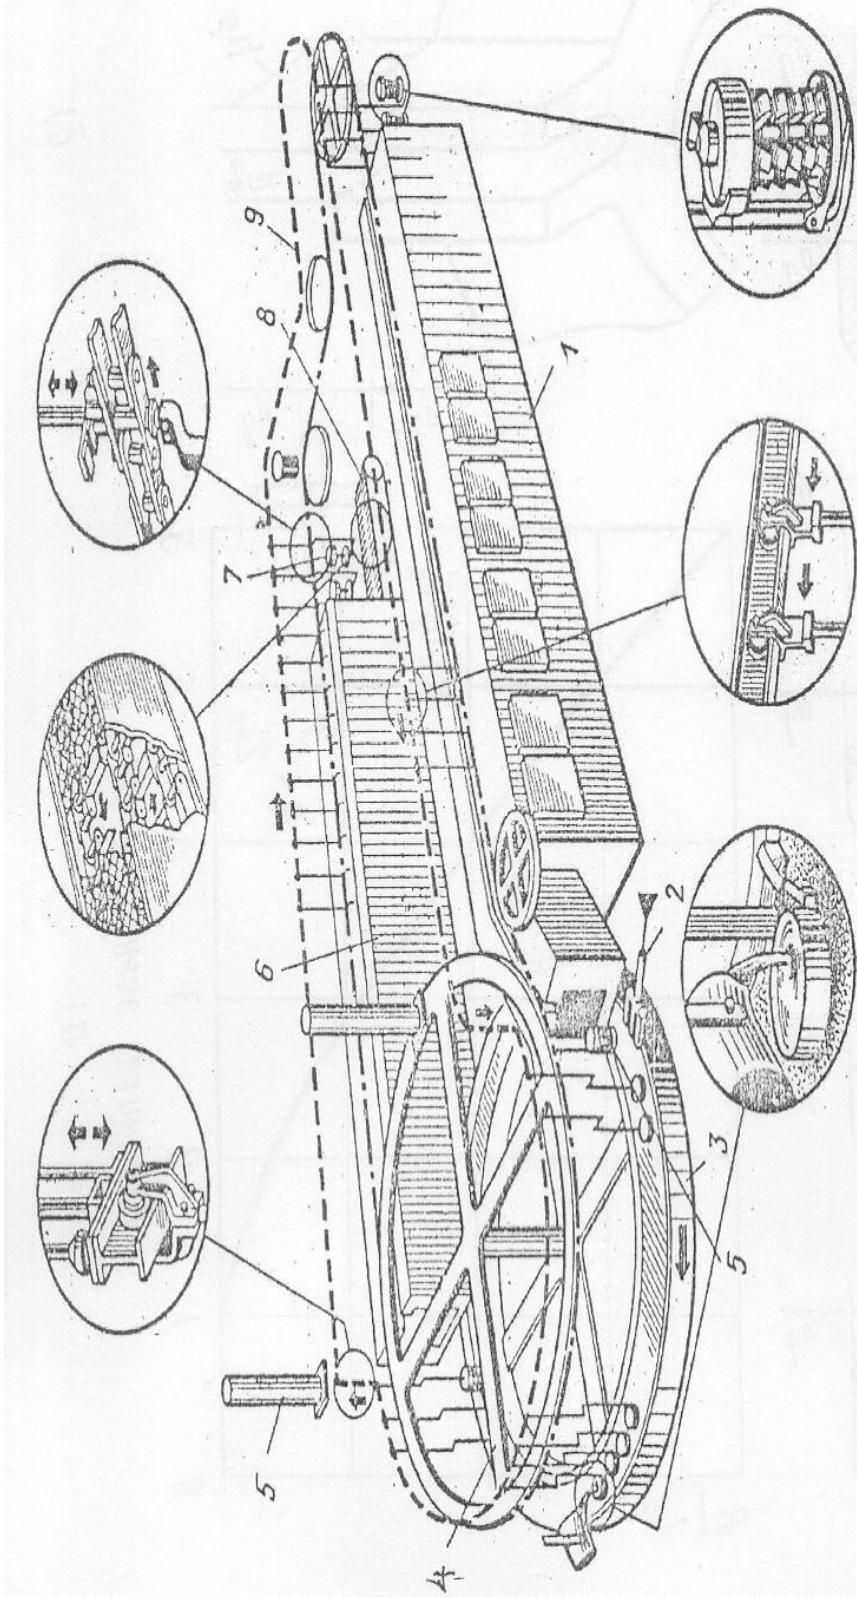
Схема агрегата для прокаливания, формовки, заливки и выбивки оболочковых форм: 1 – газовая печь; 2 – трубы для создания зоны кипящего слоя песка; 3 – заливочная карусель; 4 – звездочка привода цепного конвейера; 5 – пневматические устройства для спуска оболочковых форм в опорный материал в зоне кипящего слоя и извлечения блока затвердевших отливок; 6 – охлаждательная камера; 7 – блок отливок на позиции очистки от остатков керамики; 8 – конвейер для удаления остатков керамики; 9 – конвейер.
